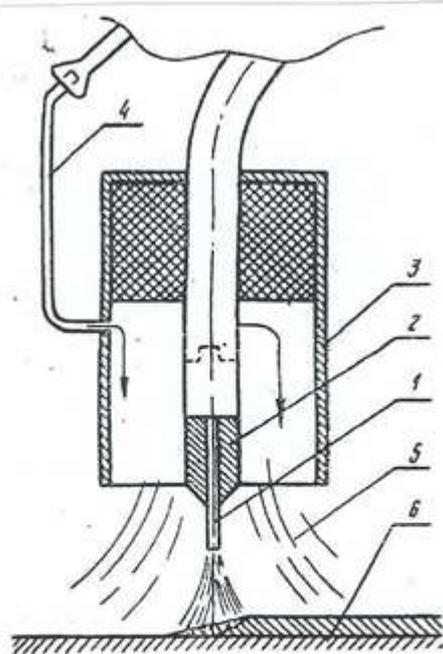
Схема сварки в углекислом газе: 1 — электрод; 2 — горелка; 3 — сопло; 4 — трубка для подачи углекислого газа; 5 — углекислый газ; 6 — свариваемое изделие.
